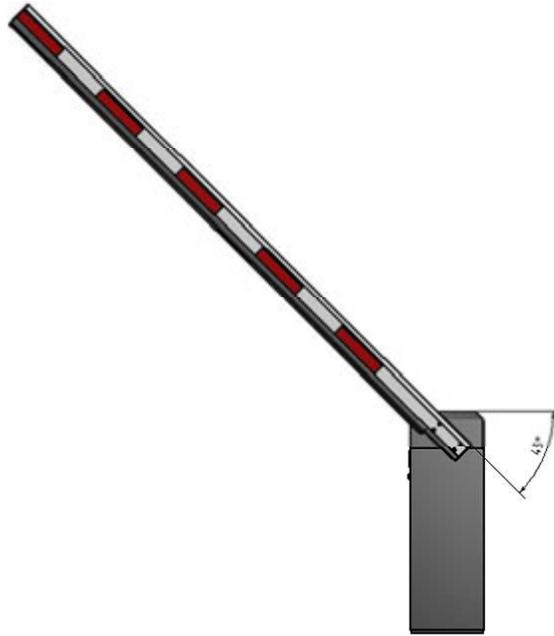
Angle d'ouverture du bras de barrière 45°
